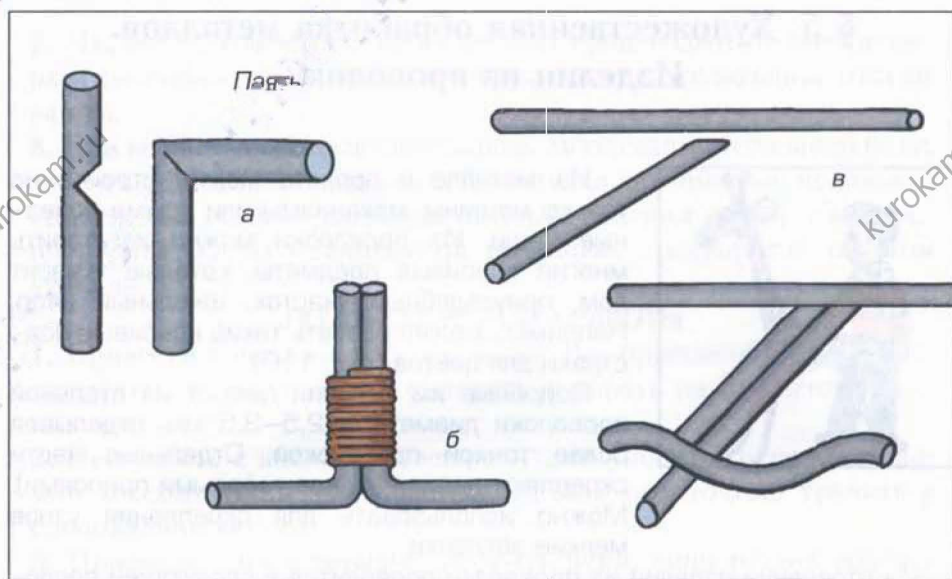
Стыковка деталей из проволоки: а – сгибание под углом, б – скрутка деталей мягкой проволокой перед пайкой, в – соединение концов деталей из проволоки
